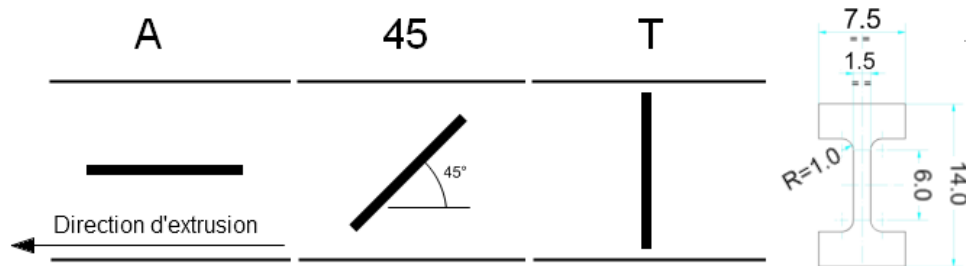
Schéma illustrant les trois directions de prélèvement des éprouvettes et dimensions des éprouvettes de traction. Dimensions en millimètres. Epaisseur : 0,75 mm.
